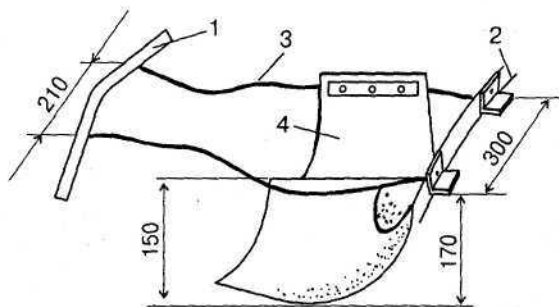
Установка трубчатых упоров: 1 — шпангоут 5; 2 — шпангоут 6; 3 — трубчатые упоры; 4 — банка
